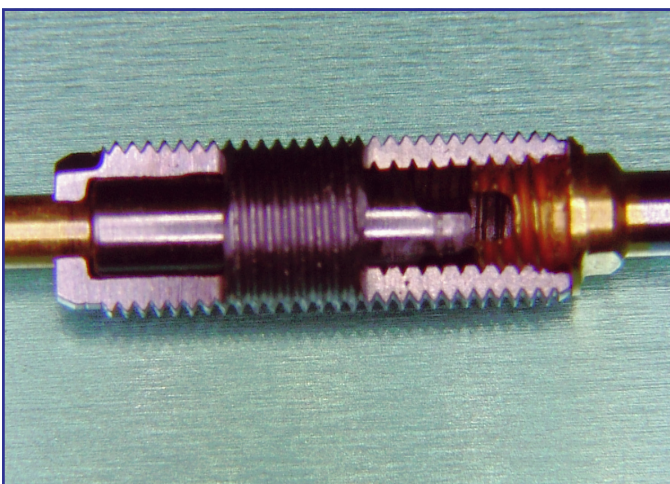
2. Prototyp - Wurzelanker und Gewindeschaft
